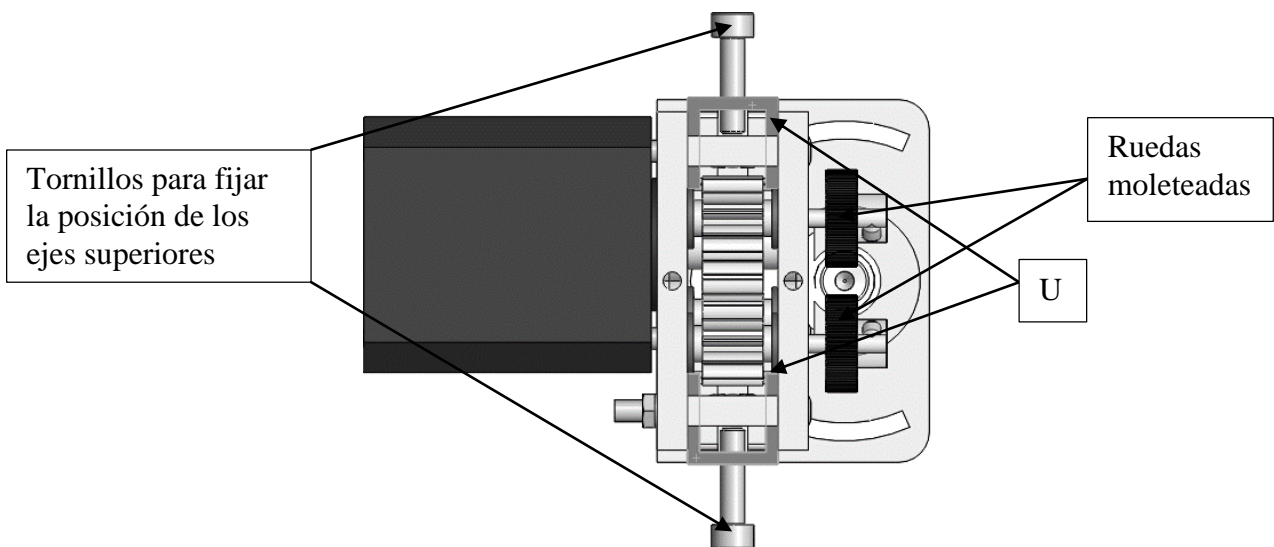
Sistema de regulación de presión del extrusor de engranajes pivotantes (Versión 01)
